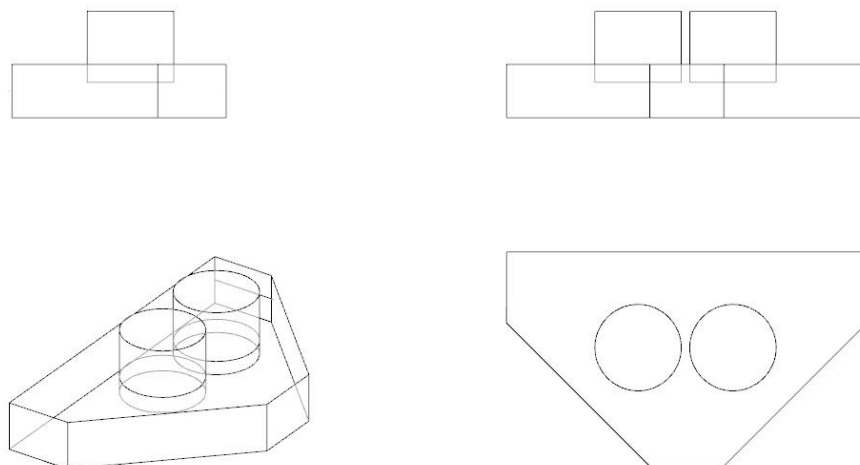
Esquema de planta hexagonal. Ilustración sin escala.
